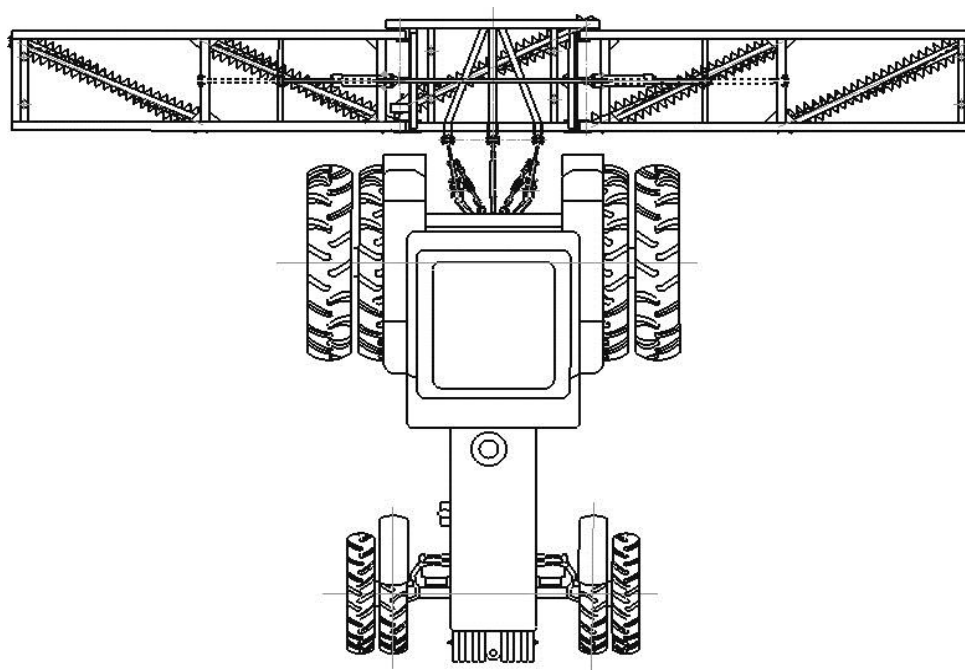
Усовершенствованный фрезер пассивного типа ФПТ-09А с трактором (вид сверху).
